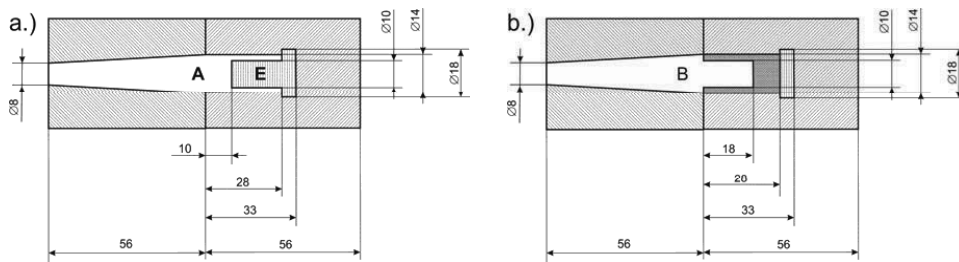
Herstellung eines gradierten Bauteils an einer konventionellen Spritzgussmaschine durch Einlegeteile a.) Einspritzen des Feedstocks A mit Platzhalter, Einlegeteil E b.) Einspritzen des Feedstocks B ohne Platzhalter.
